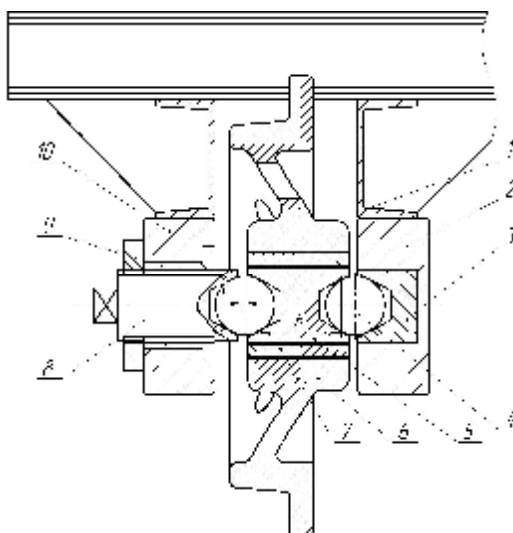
Колесо шахтной вагонетки с дополнительной кинематической подвижностью:
